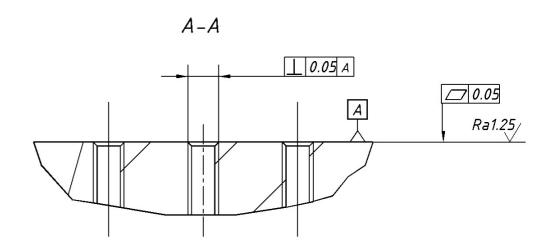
Разметка установочной площадки ВИП-301-С (трехточечное крепление)
